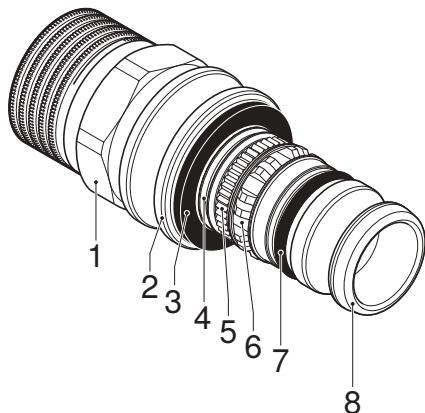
Конструкция переходника Geberit Mepla с резьбой из металла
